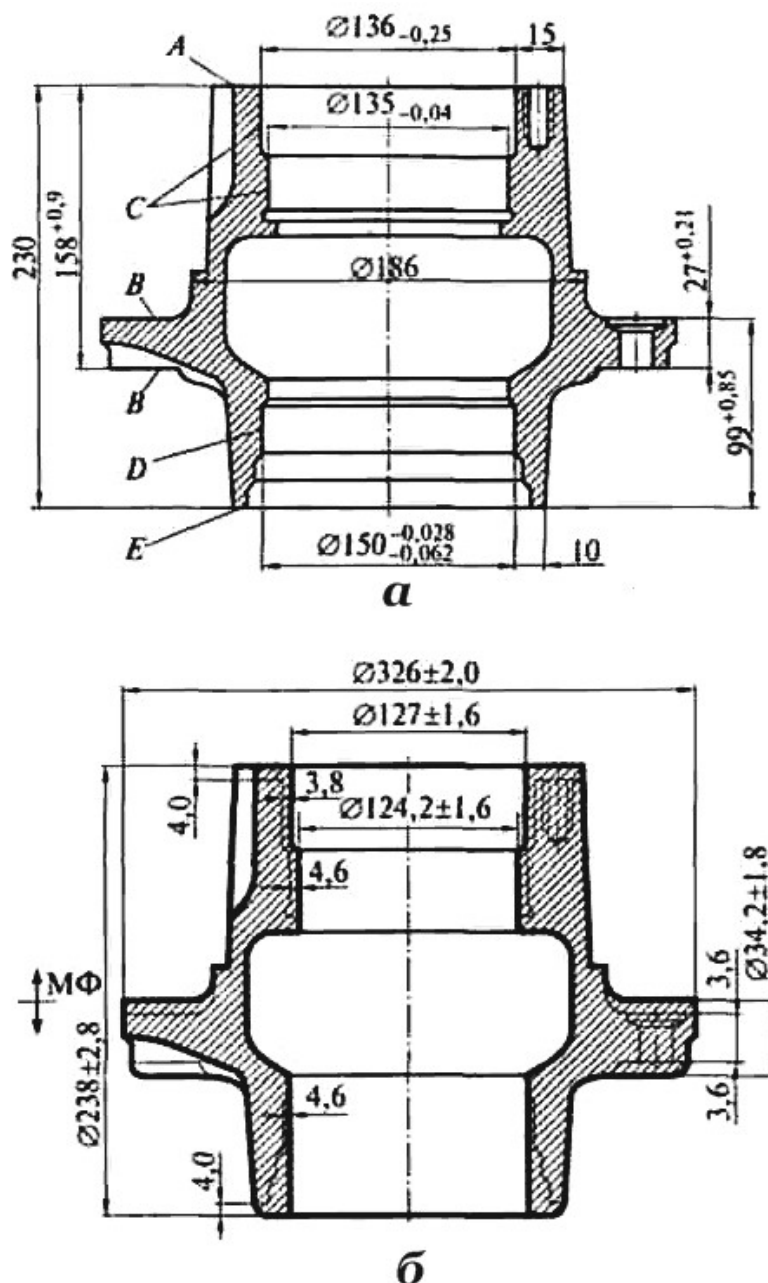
Чертеж детали (а) и отливки (б) ступицы заднего колеса: МФ – разъем модели и формы; А, В, С, D, E – обрабатываемые поверхности
